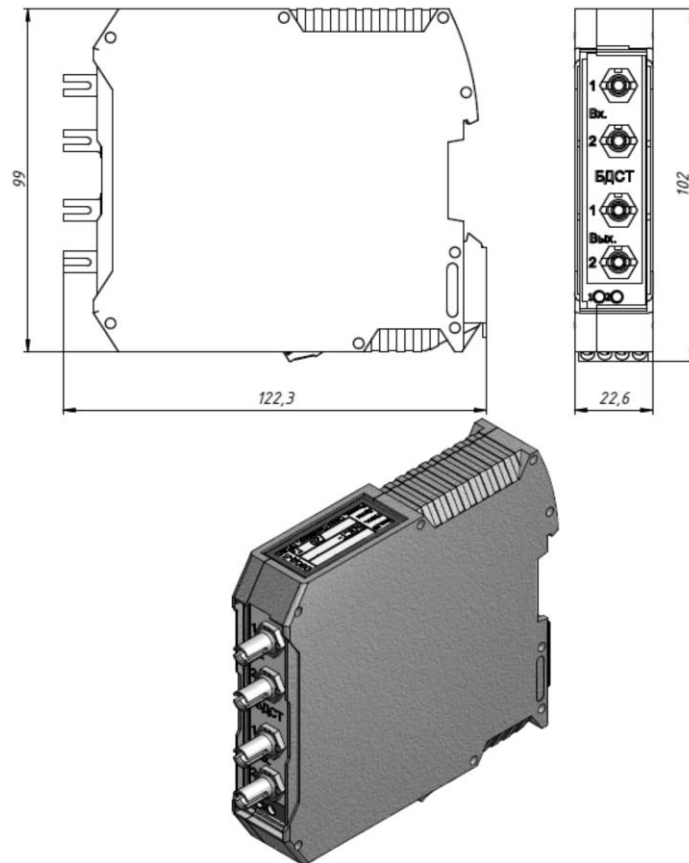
Внешний вид и габаритные размеры БДСТ
